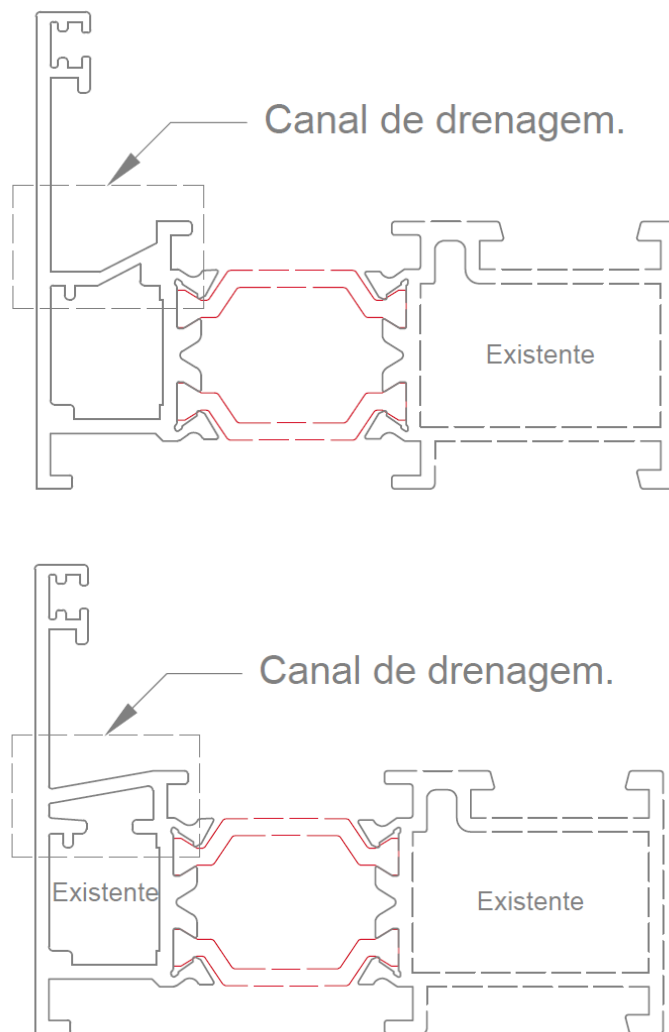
Esboço 3 (em cima) comparado com o perfil já existente (em baixo).
